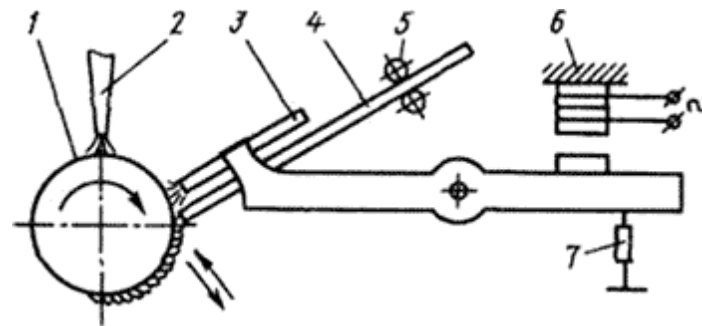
Схема вібрودугового наплавлення деталей
